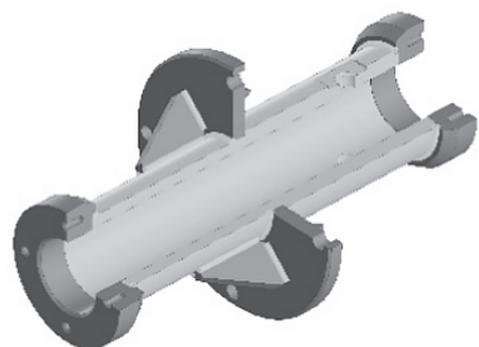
Сварная сборочная единица «Корпус»
